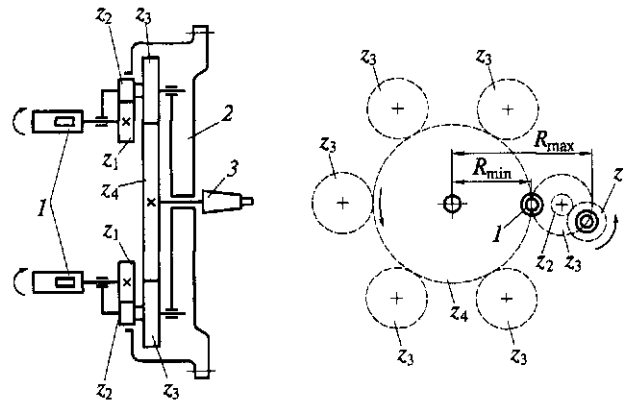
Схема инструментальной насадки для сверлильных работ с регулируемыми шпинделями:
